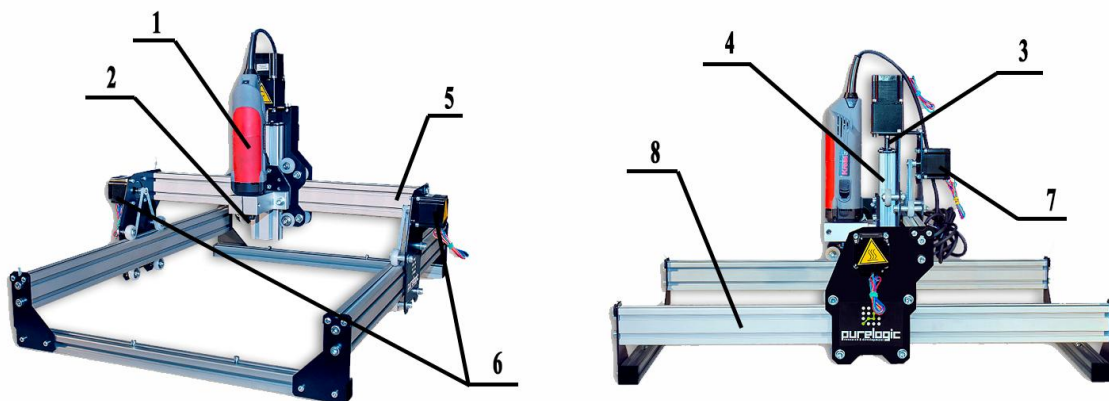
Фрезерно-гравірувальний станок Hobby
